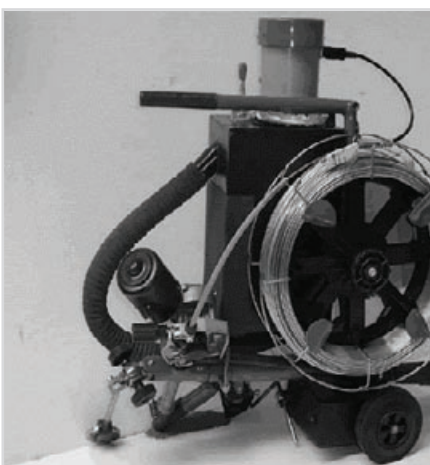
Автоматическая сварка металлов плавящимся электродом под слоем флюса. Сварочный трактор
